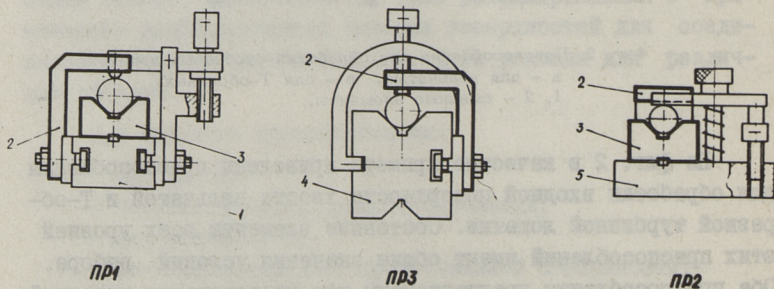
Приспособления для обработки турбинных лопаток:
